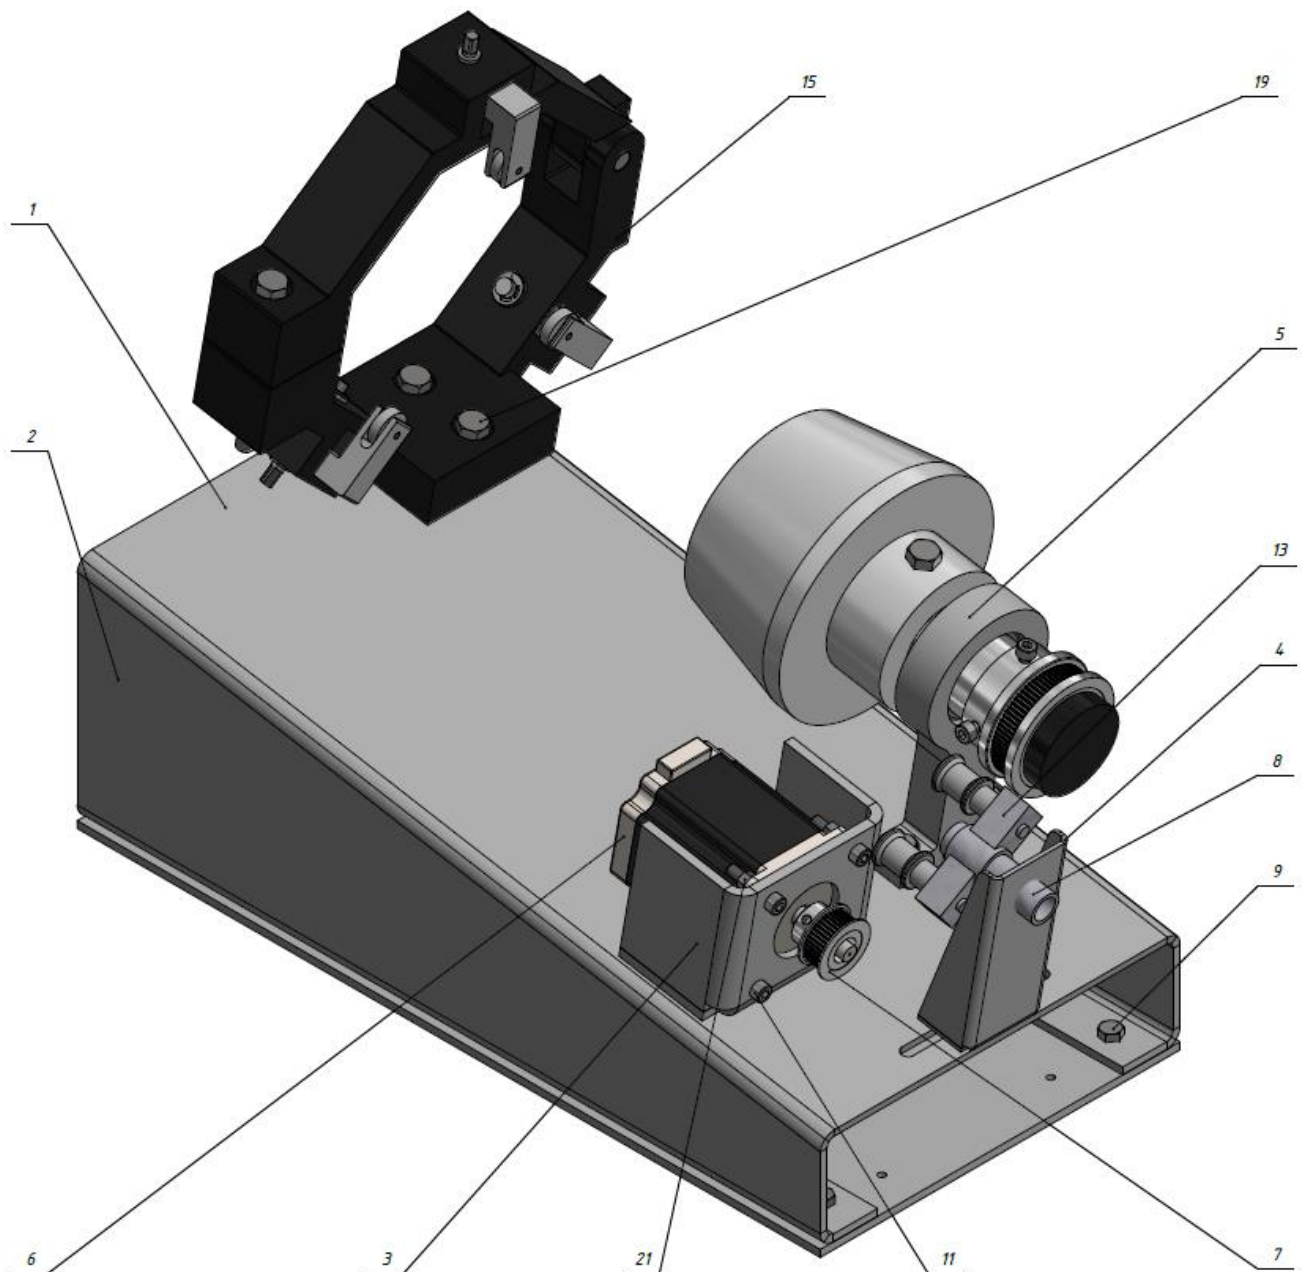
3D – модель додаткового приводу повороту заготовки.
